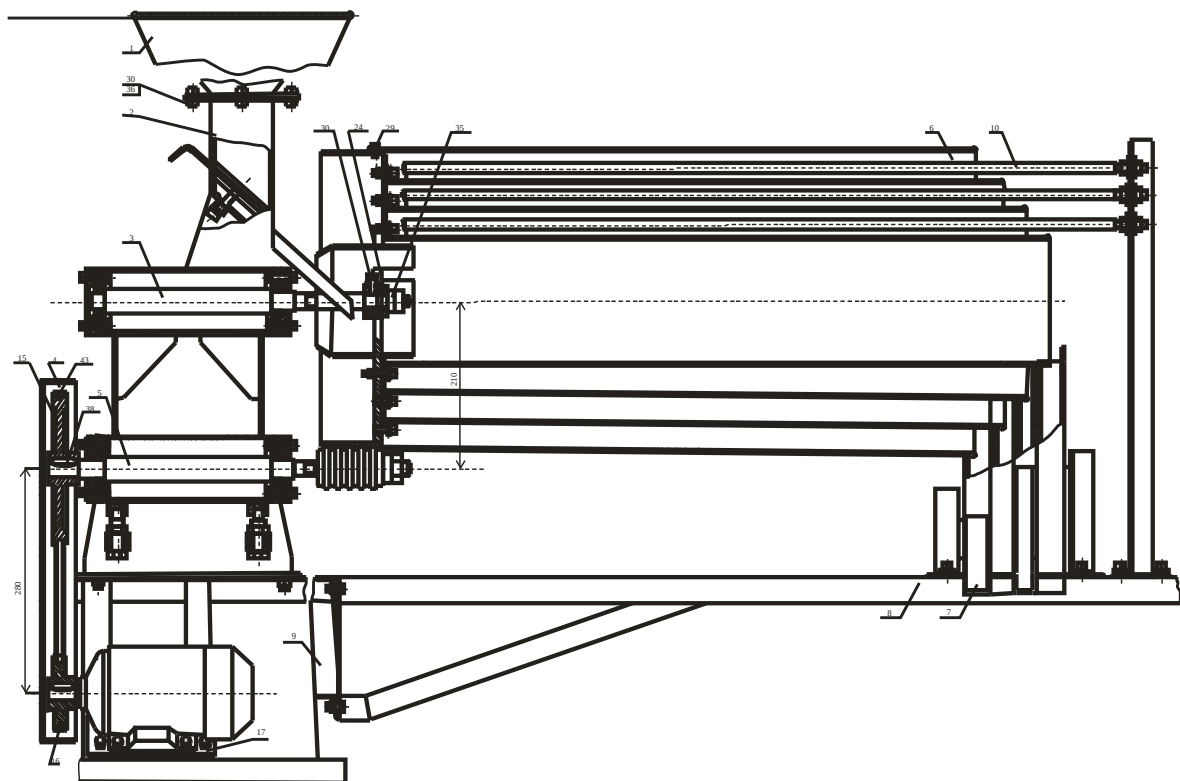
Установка МСС-1 для сортировки и калибровки зернопродуктов
